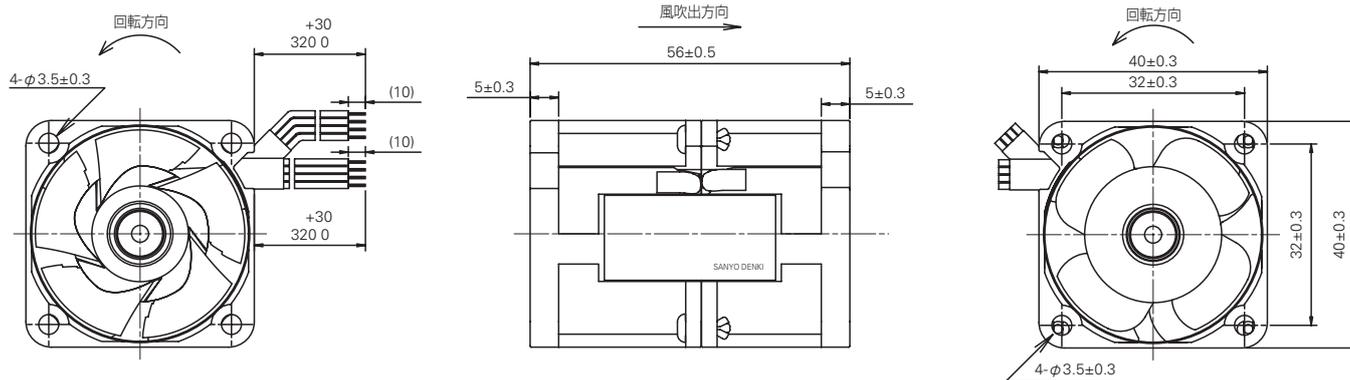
40mm角56mm厚CREタイプの寸法諸元 (単位: mm)
